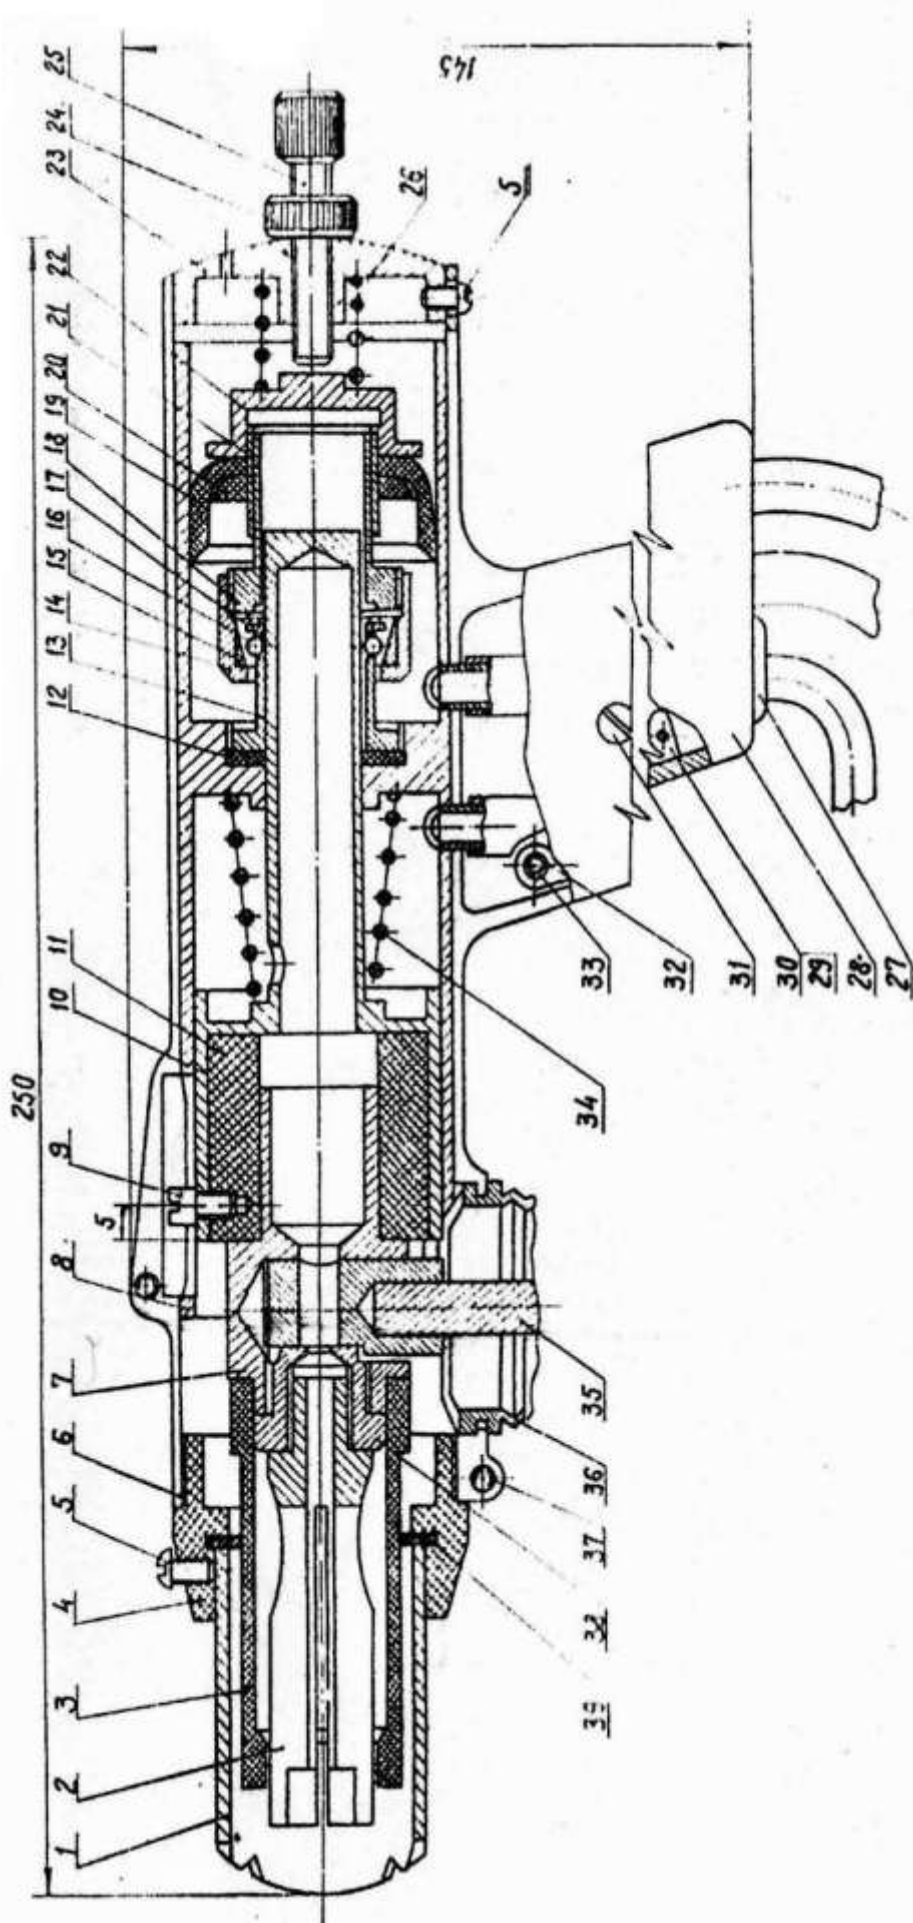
Пистолет для приварки шипов в защитных газах и установке УБ-1-2:
